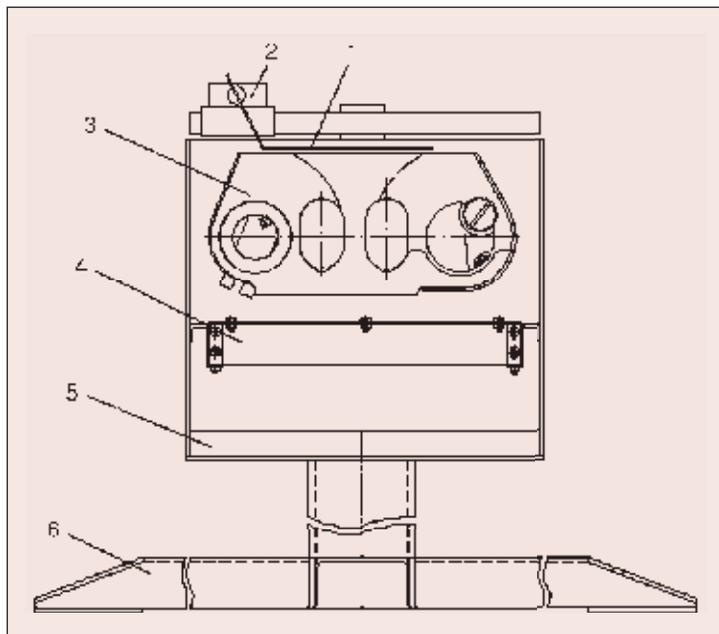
Активный пост установки для наплавки звеньев: 1 — составной электрод; 2 — электрододержатель; 3 — наплавляемое звено; 4 — флюсоборник; 5 — наплавочный пост; 6 — опорная стойка
